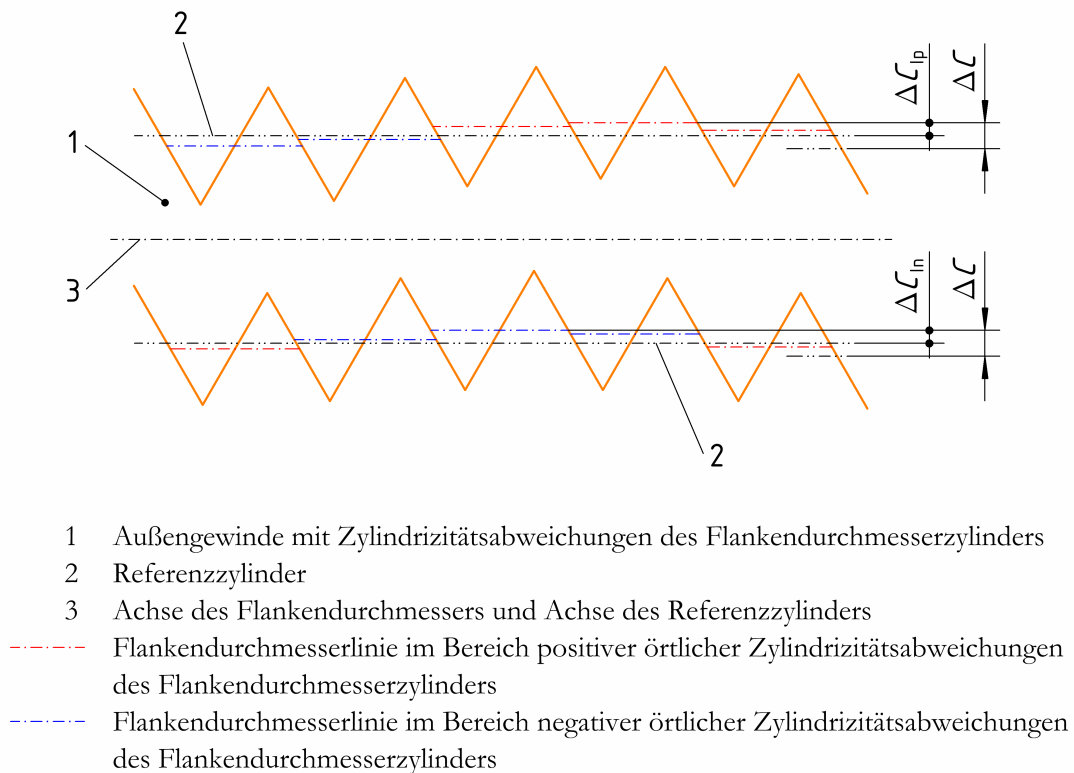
zylindrisches Außengewinde mit Zylindrizitätsabweichungen des Flankendurchmesserzylinders
